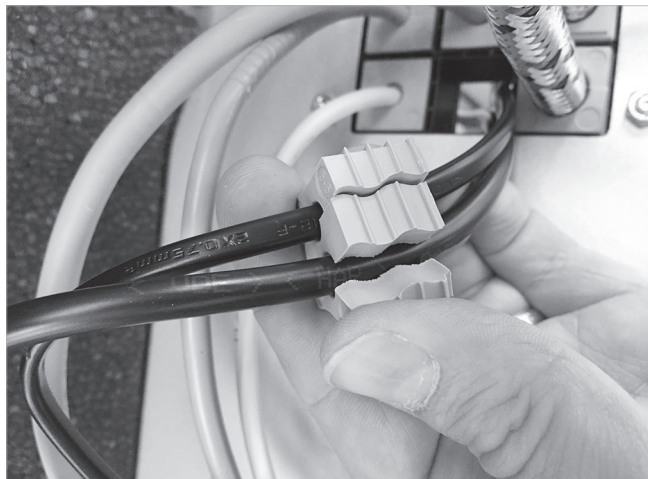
Posizionamento del passaggio cavo attorno al cavo
